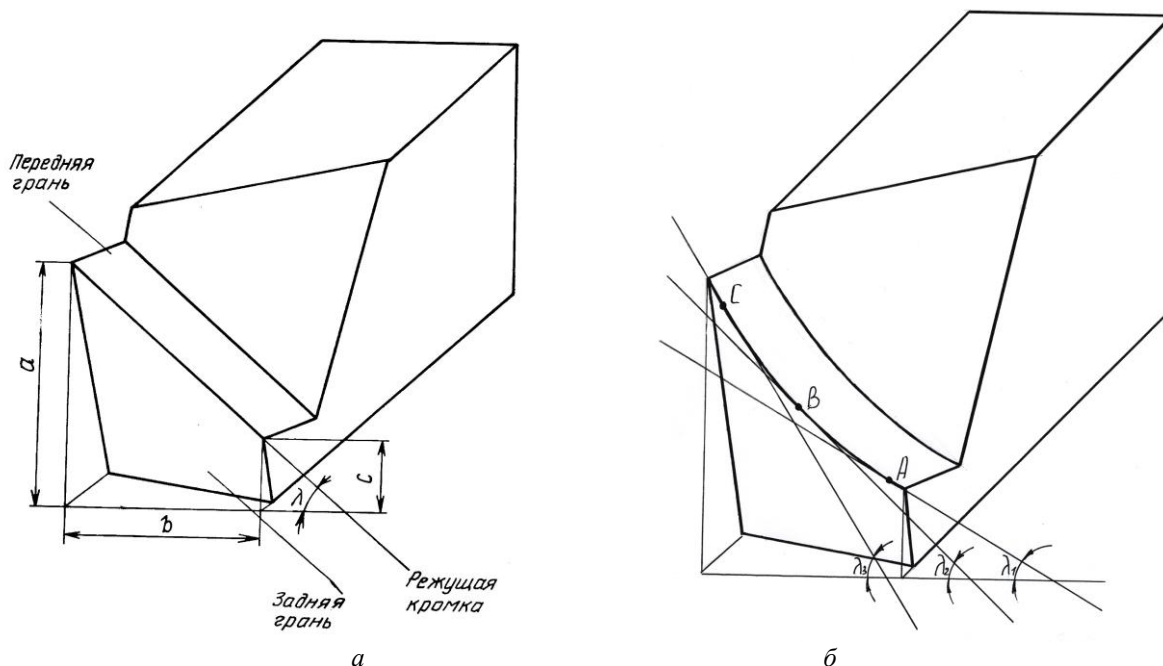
Конструкции безвершинных резцов: а – базовая конструкция; б – прогрессивная конструкция с регулируемым углом наклона кромки
